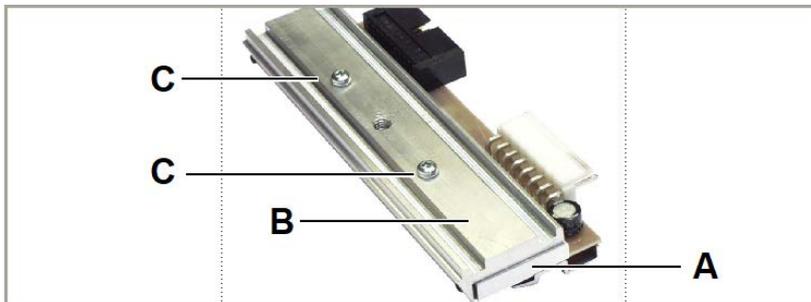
Druckkopf (A) und Halterung (B) wurden mit speziellen Positionierungswerkzeugen exakt ausgerichtet.
